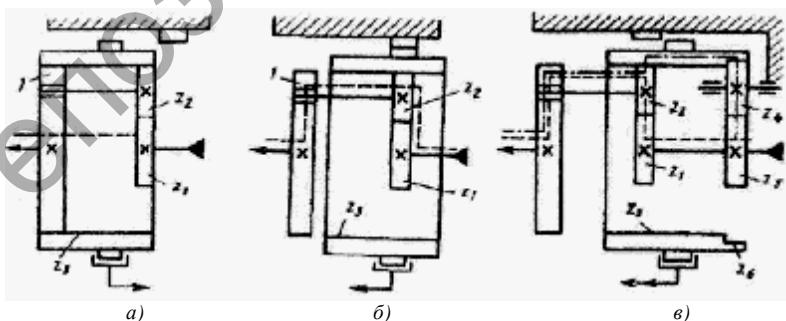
Схемы совмещенного привода главного движения и привода подачи токарного станка
